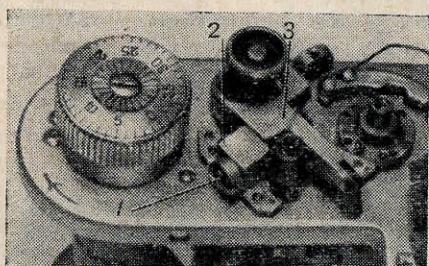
Основной рычаг установки зеркала в аппарате «Зенит» (вид со стороны объектива)
